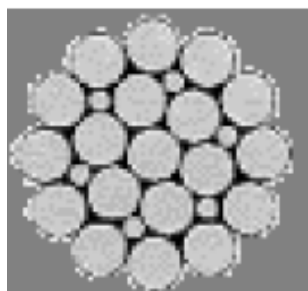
Cable tipo Filler-wire
